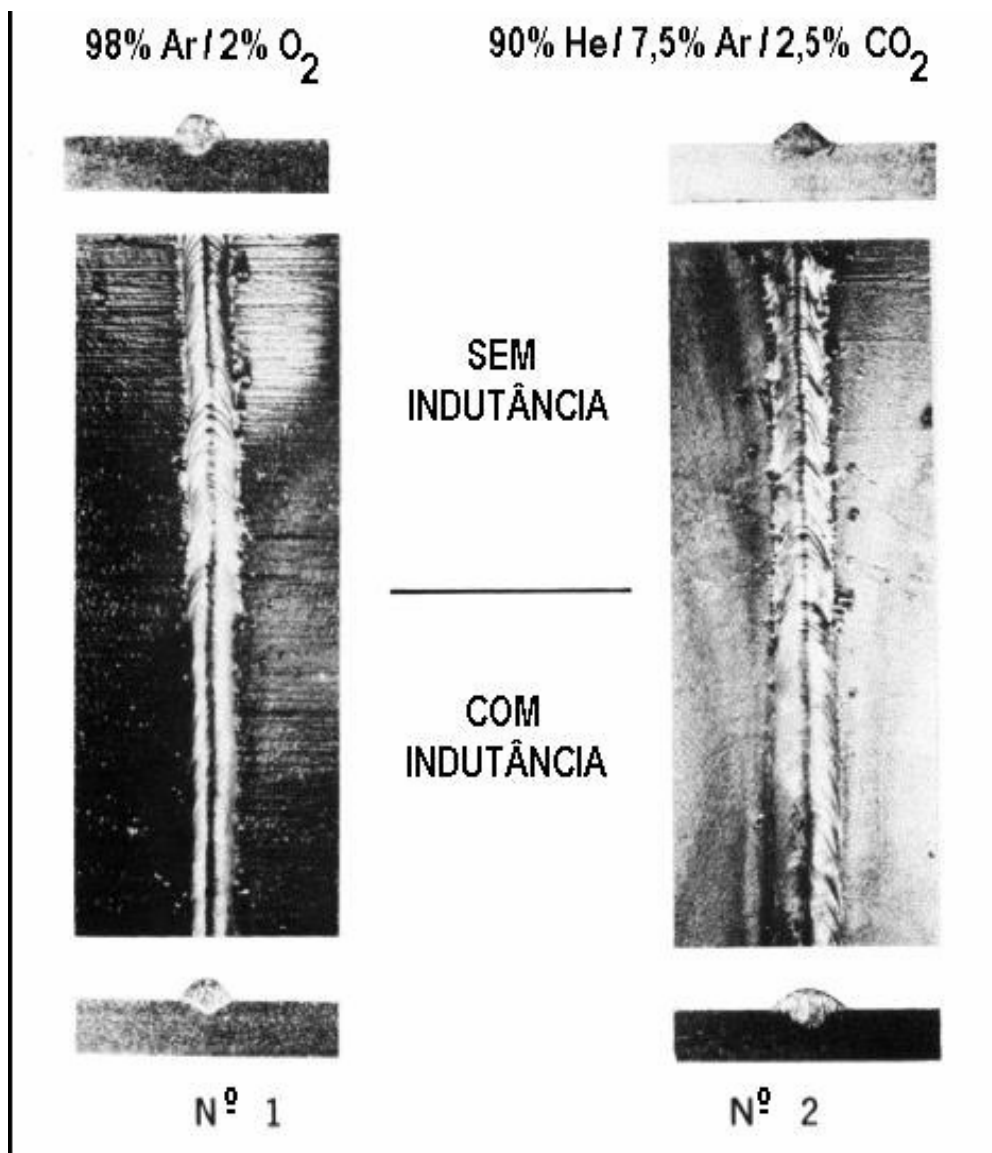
Efeito da indutância no aspecto do cordão de solda (MIG/MAG WELDING, 2003).
